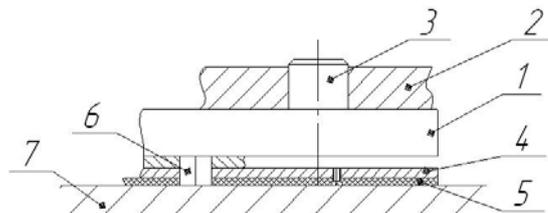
Схема установки кассеты на каретке координатного механизма полуавтомата JАСК JK-3020
